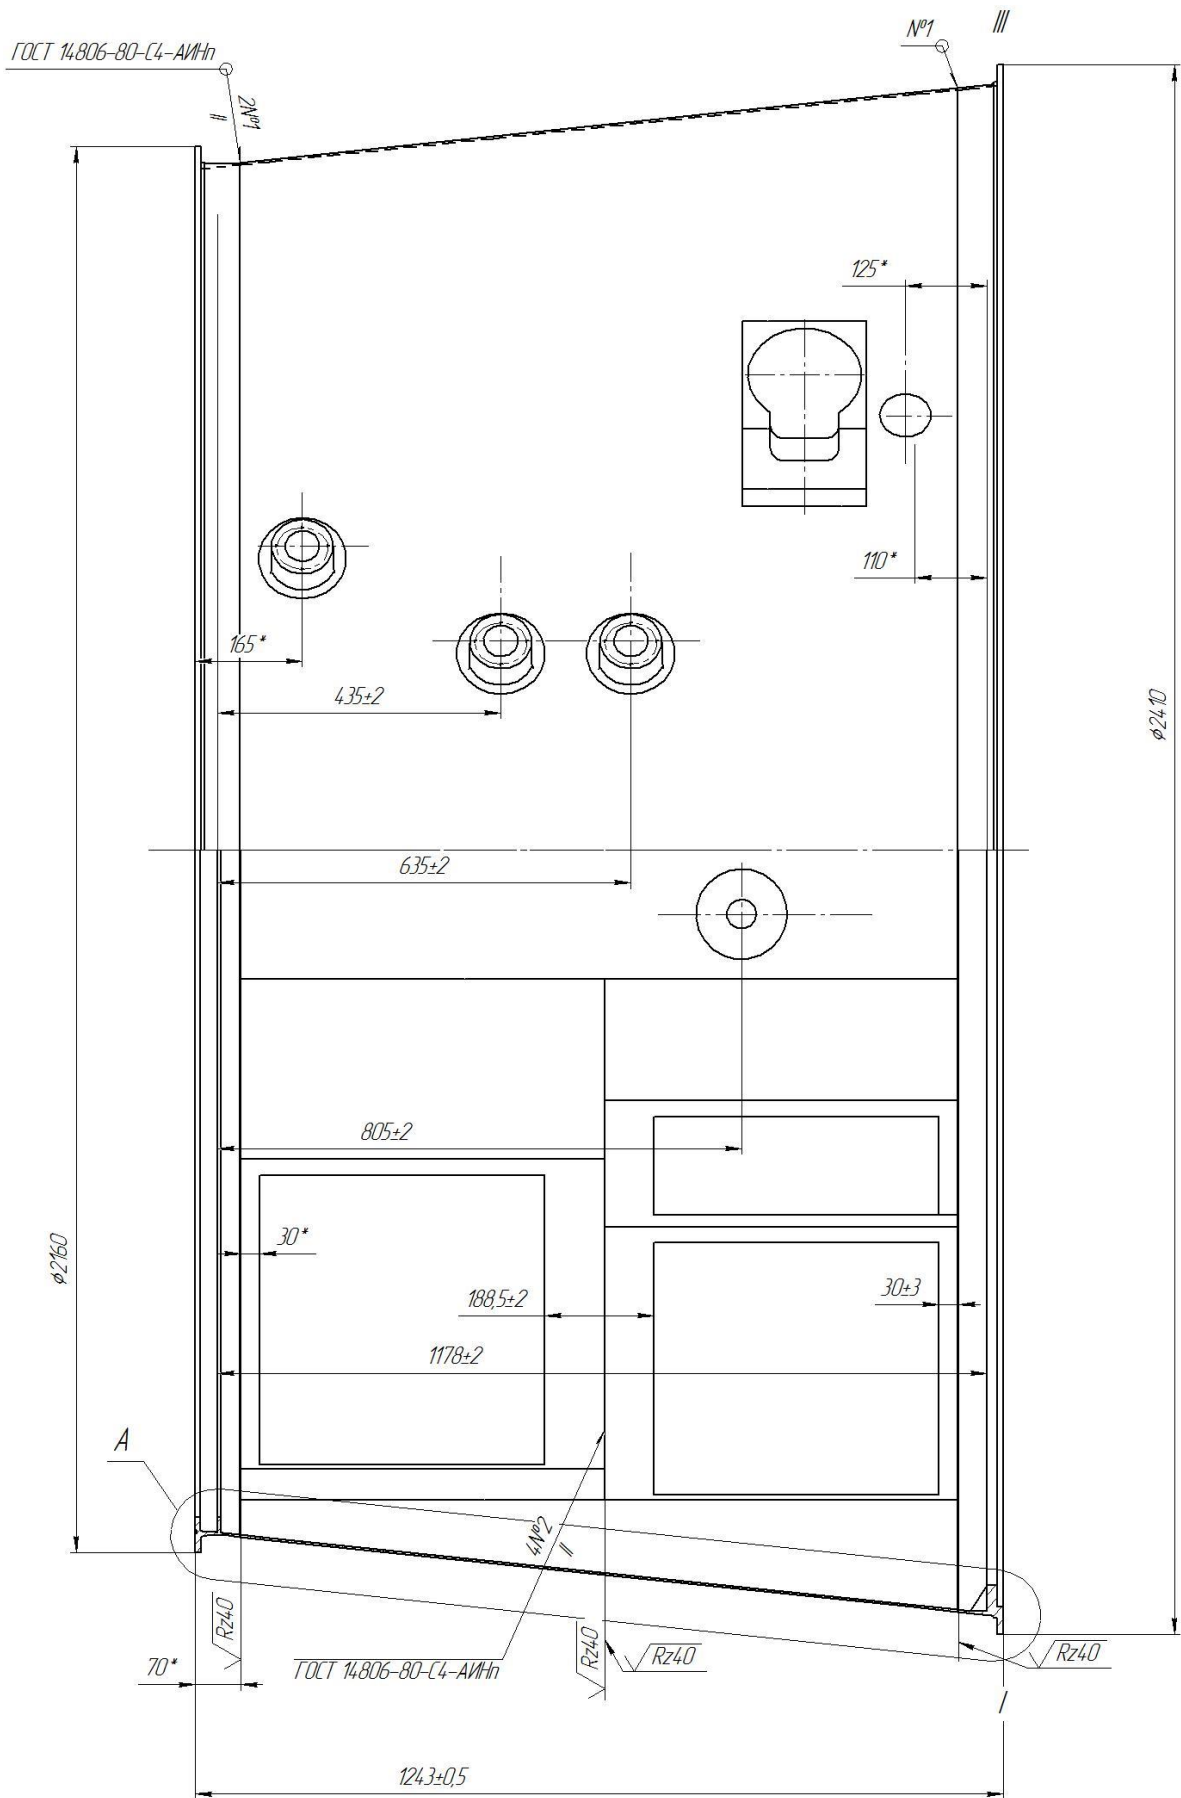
Сварка швов корпуса приборного отсека
